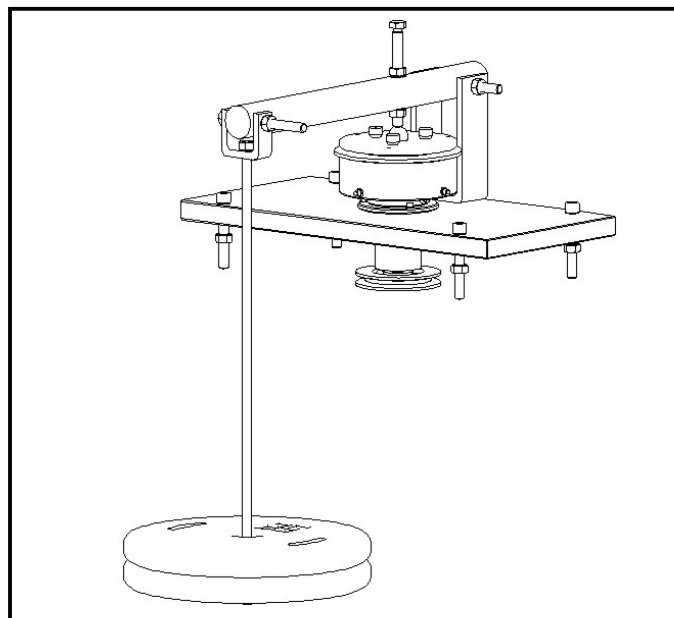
Perspectiva do conjunto do segundo equipamento.
